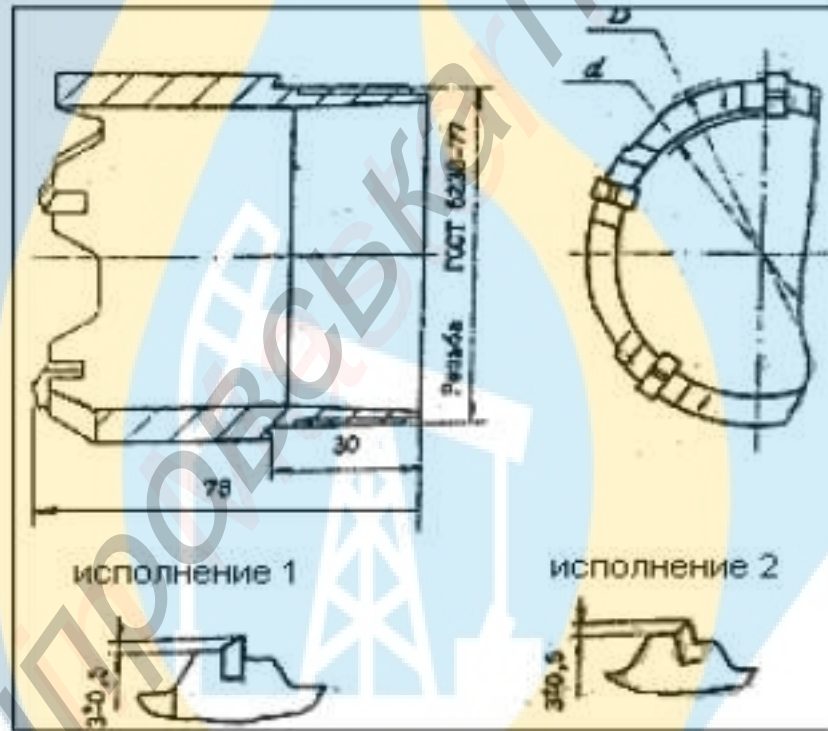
Твердосплавна коронка типу CM9.
